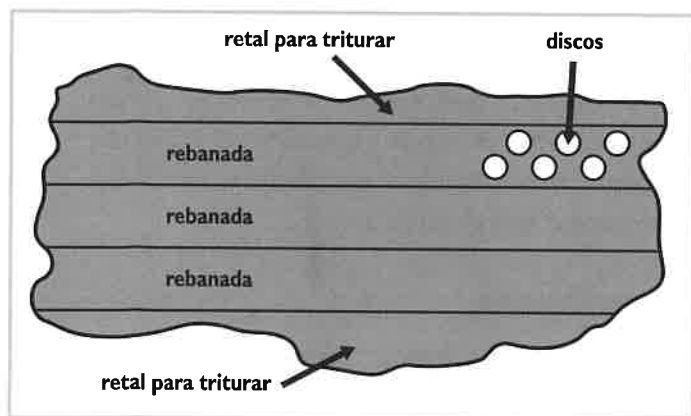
Plancha de corcho delgada para la fabricación de discos.
